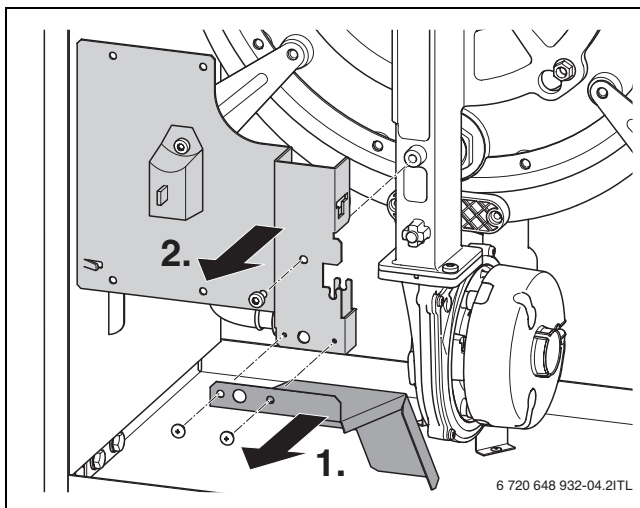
Smontaggio di lamiera di protezione dallo sgocciamento lamiera di bloccaggio
